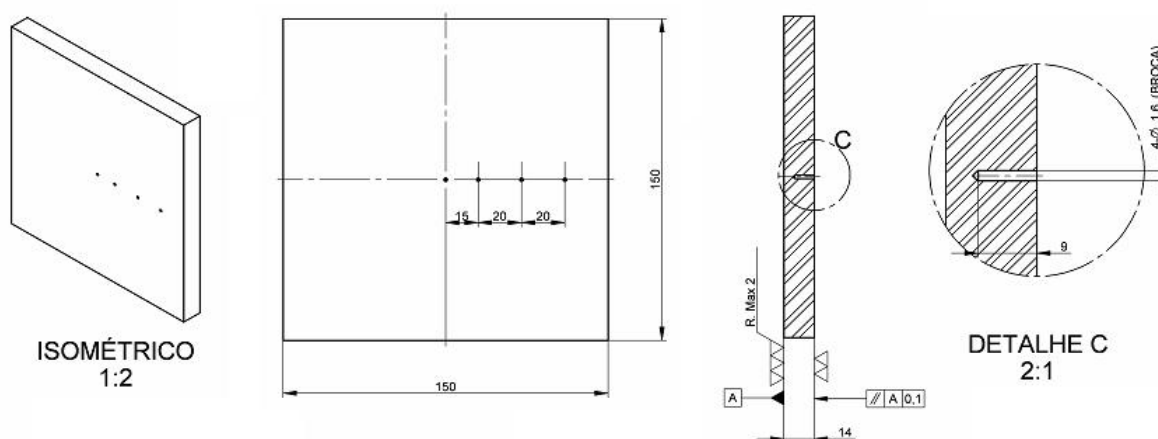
Desenho detalhado para fabricação da placa 06 com dimensões de 150 mm de largura por 14 mm de espessura. O detalhe “C” mostra o diâmetro e profundidade dos furos.
